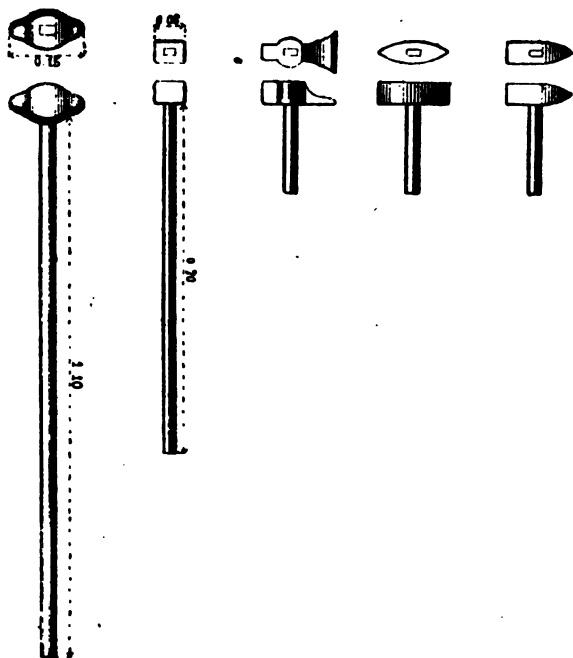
à 748. Massettes et marteaux du scheideur (plans et élévations).
